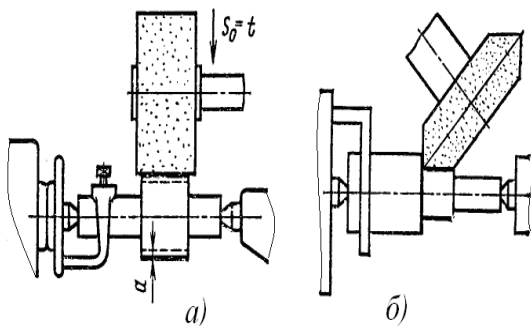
Схема круглого шліфування з поперечною подачею (а); схема шліфування шийки й виступу вала (б)
